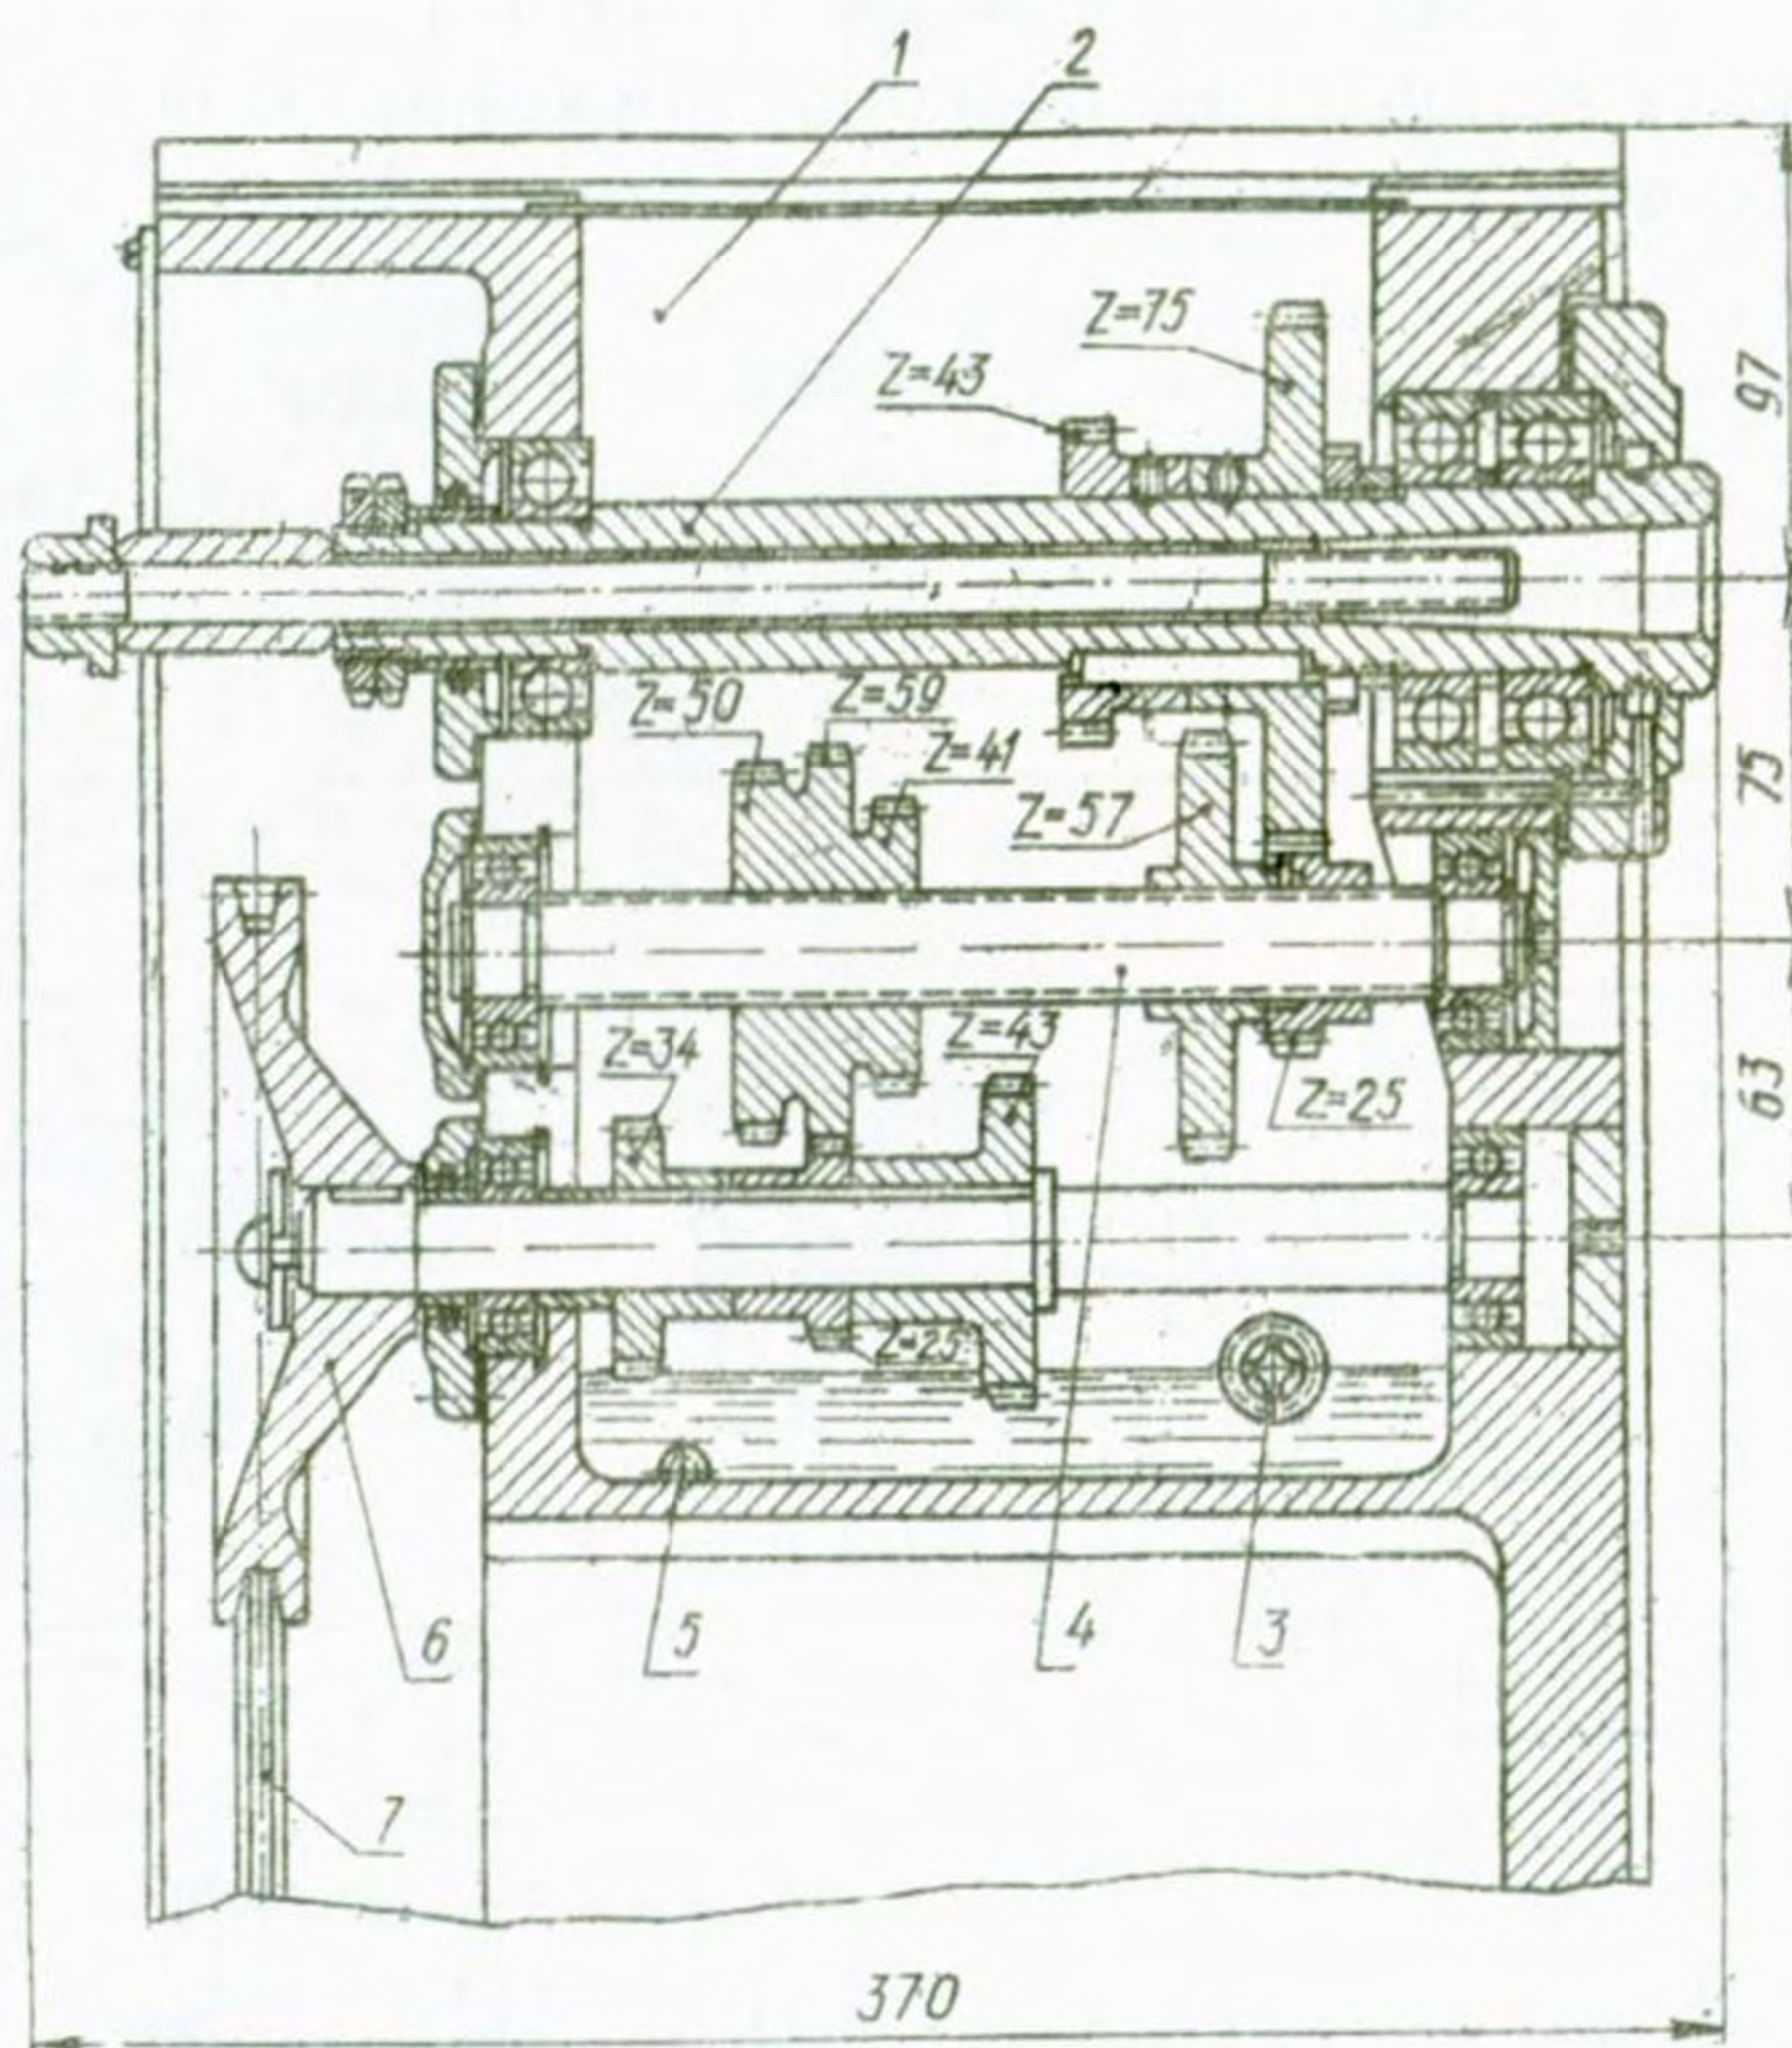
Розріз коробки швидкостей фрезерного верстата НГФ – 110 ШЗ: 1 – корпус коробки; 2 – шпиндельний вал; 3 – отвір для заливання масла; 4 – шліцьовий вал; 5 – зливний отвір; 6 – шків на первинному валі; 7 – клинопасова передача, Z – кількість зубців на зубчастому колесі
